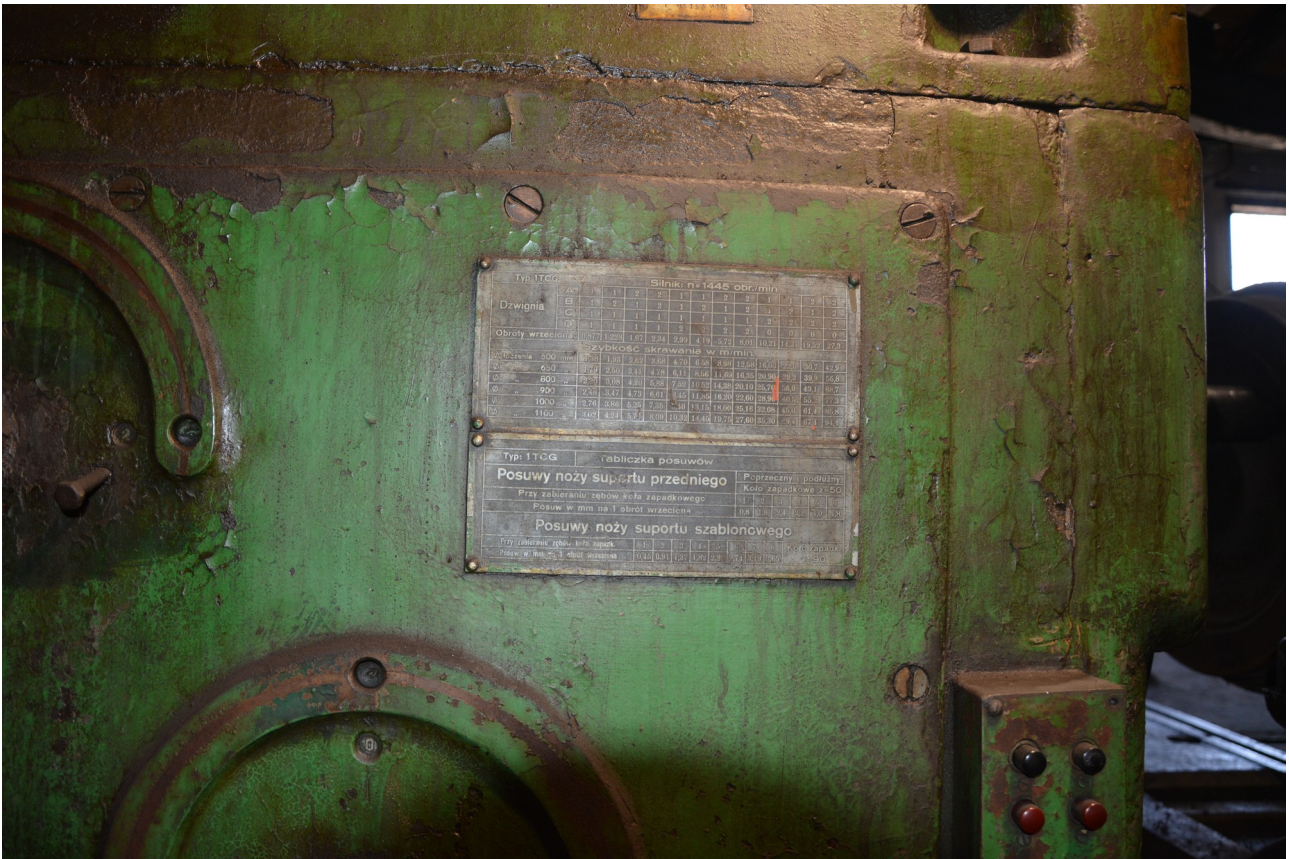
Stan zachowania przed rozpoczęciem prac – 2023 rok
